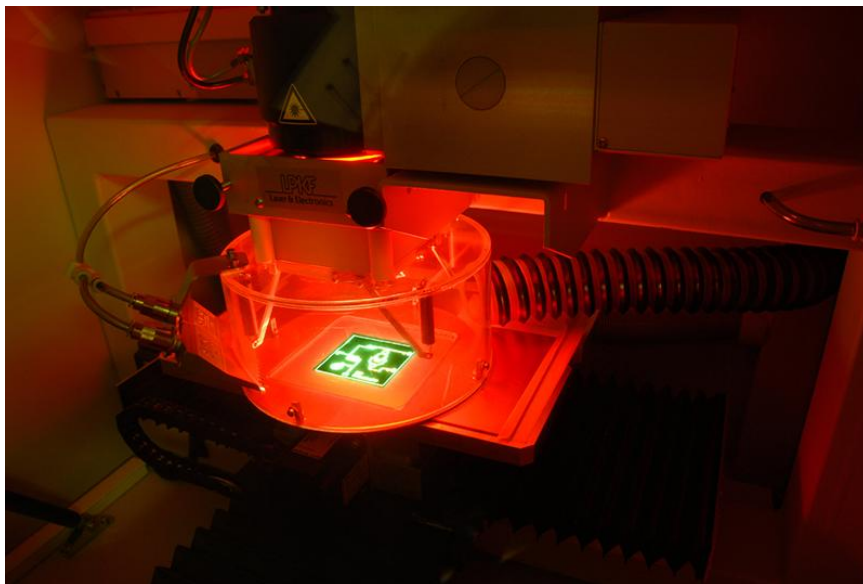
Photographie de la fabrication de circuit par la machine LPKF protoLaser S.
